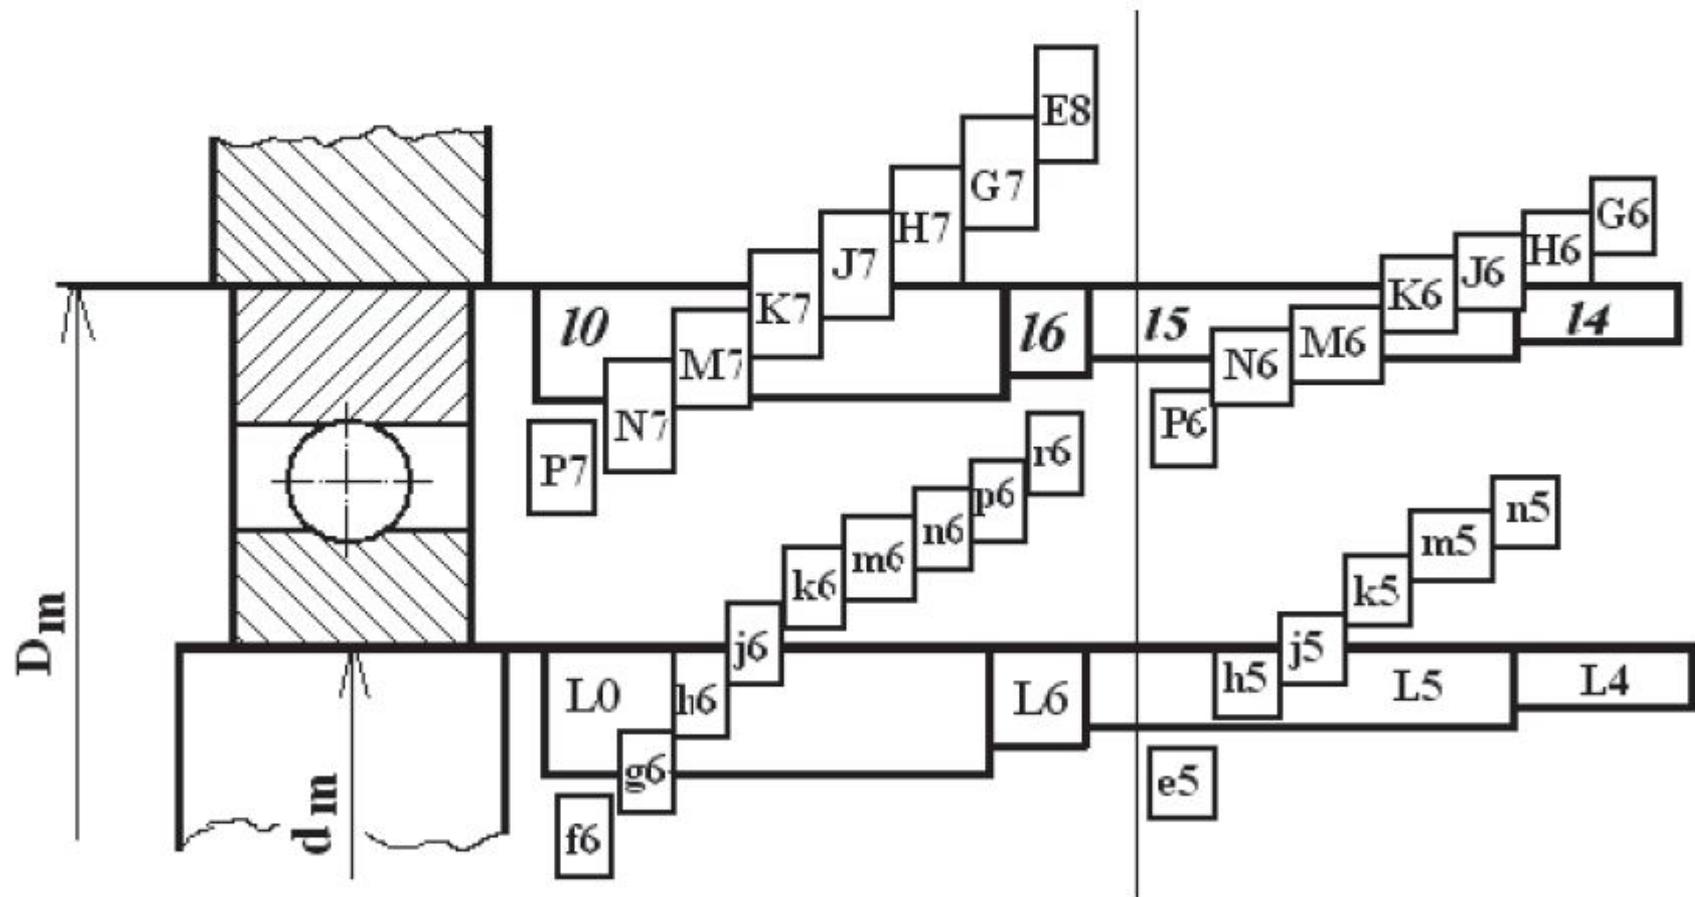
Поля допусков деталей подшипникового соединения
